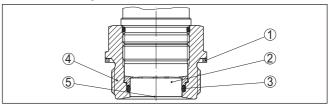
Frontbündiger Einbau der Messzelle (Beispiel: Gewinde G1½)
